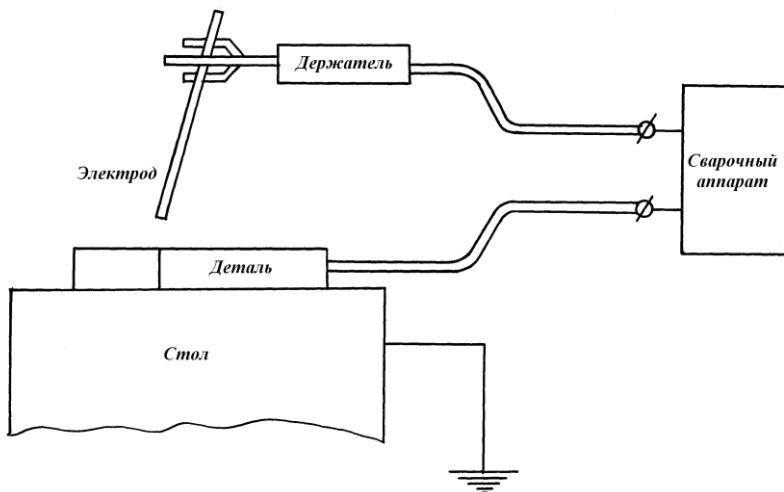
Схема поста ручной электродуговой сварки
